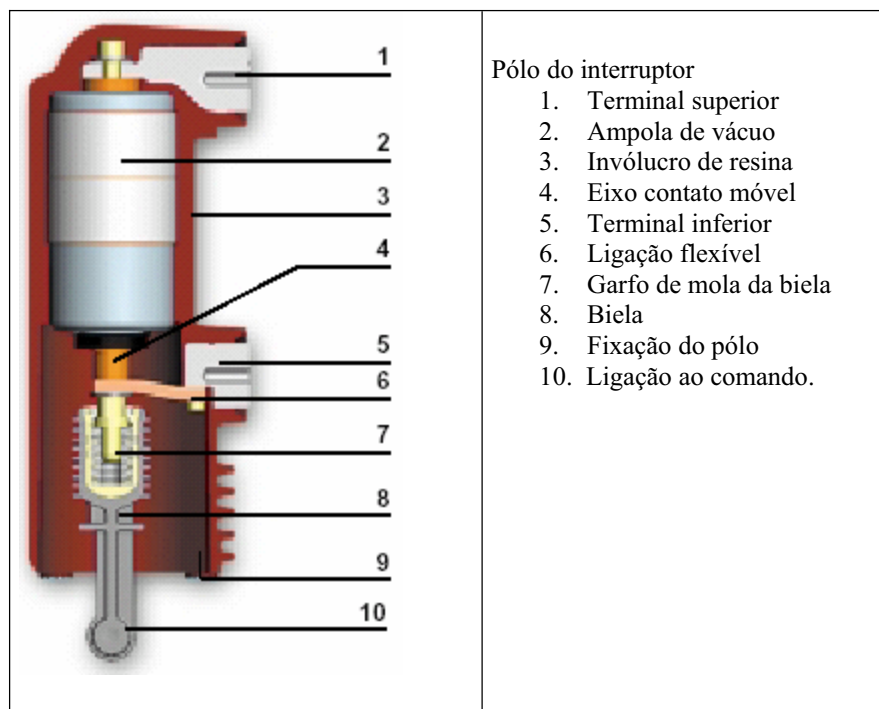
Partes integrantes de um disjuntor a vácuo
